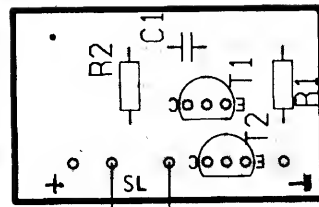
Schéma zapojení (tranzistor T1 je v tzv. univerzálním zapojení)
